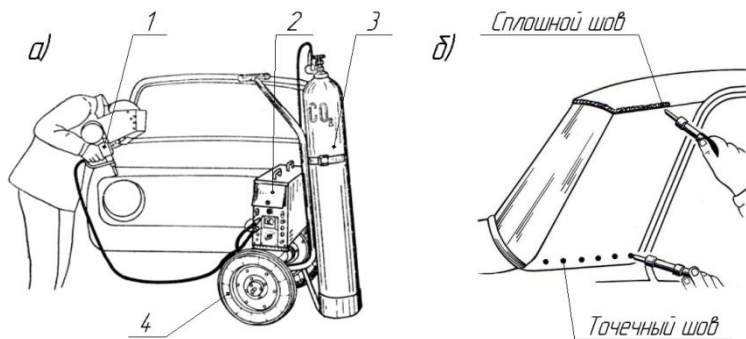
Сварка кузова в среде защитного газа при помощи передвижной установки (а) и типы применяемых швов (б):
